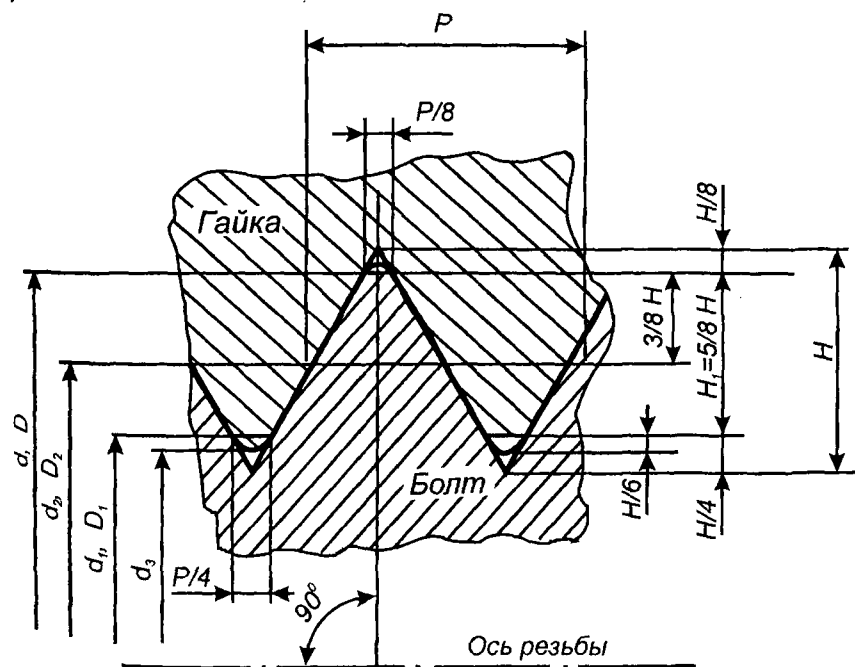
Номинальный профиль метрической резьбы и основные размеры его элементов
